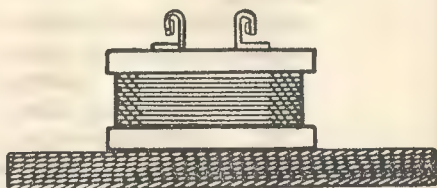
Die auf dem Grundbrett befestigte Spule mit den Lagerböcken.
